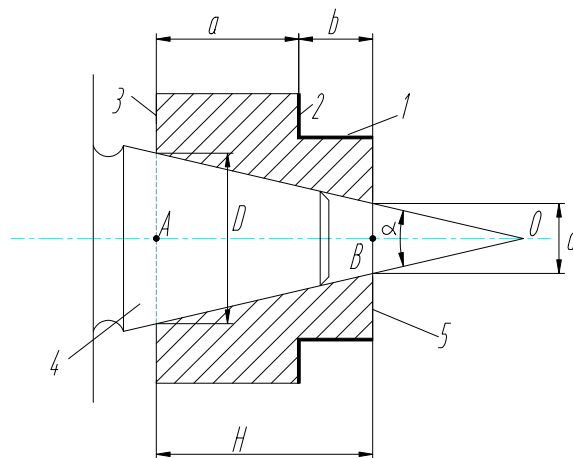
Схема базирования заготовки по конусу : 1,2,3,5 - поверхности заготовки; 4 - элемент токарного приспособления.
